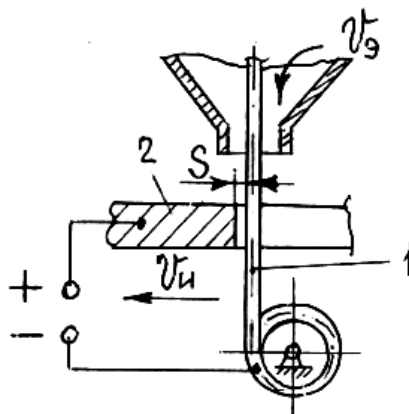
Схема розрізання непрофільованим інструментом: 1 – інструмент-електрод (дріт); 2 – заготовка
